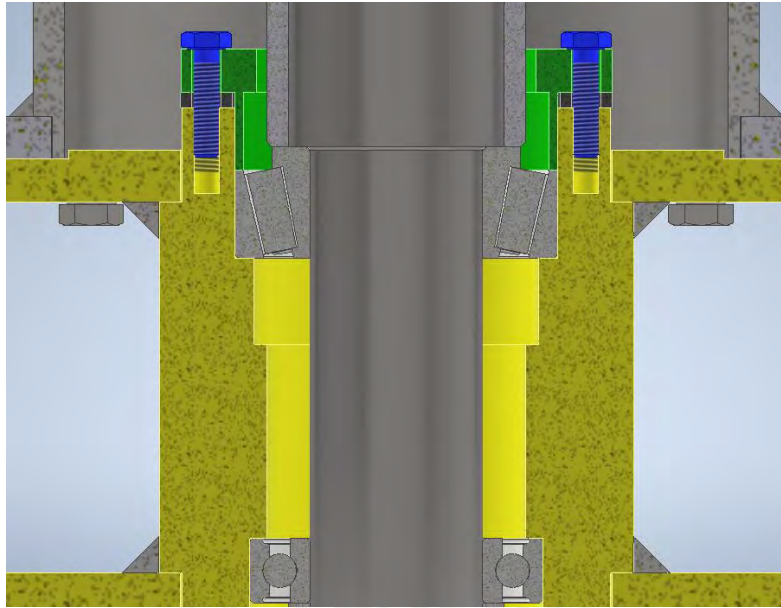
Uniones atornilladas en la tapa de rodamiento de rodillos cónicos.
